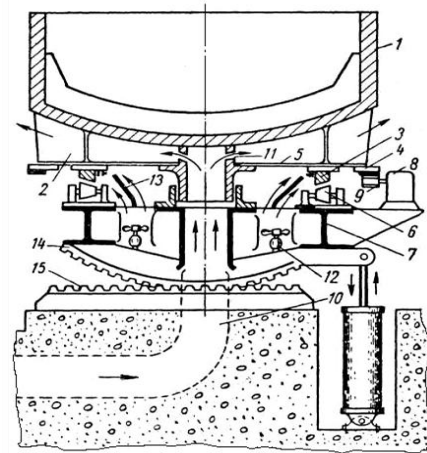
Вертикальний розріз печі РКО - 3,5 для виплавки безвуглецевого ферохрому зі змістом вуглецю $< 0,04\%$
